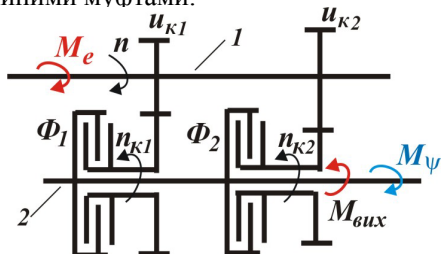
Фрагмент кінематичної схеми коробки передач:
